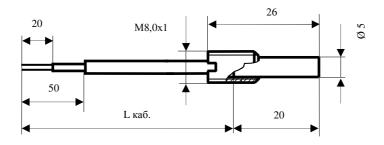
Габаритные и присоединительные размеры ТСП 002-06
